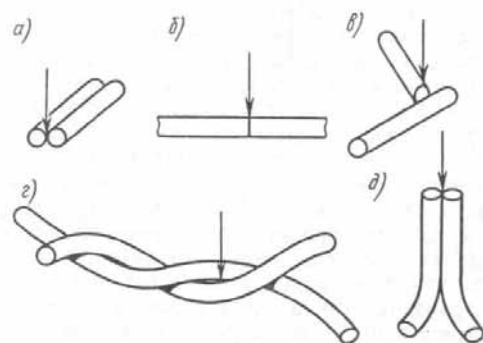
Типы сварных соединений проволоки:
